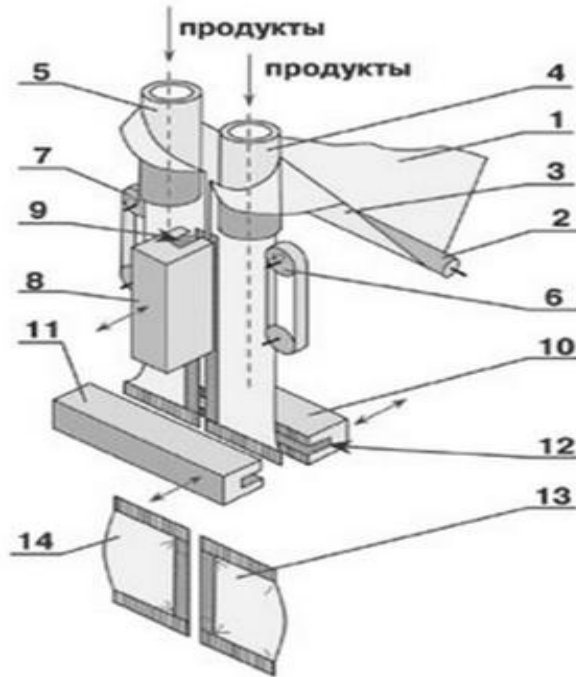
Схема двохпотокова машина із комірцем періодичної дії, з протягуючими транспортерами: 1 - пакувальний матеріал; 2 - направляючий ролик; 3 - комірць; 4, 5 - продуктопровід; 6, 7 - механізм протяжки; 8 - повздовжнє зварювання; 9, 12 - ніж; 10,11 - поперечно-зварювальні головки; 13,14 - споживча упаковка
